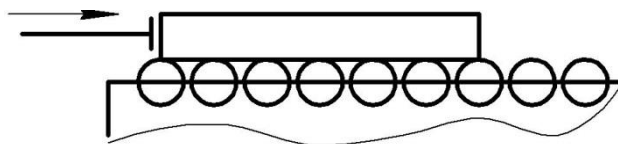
Схема позиции IV «разгрузка» четырехпозиционного роторного сборочного автомата 5
